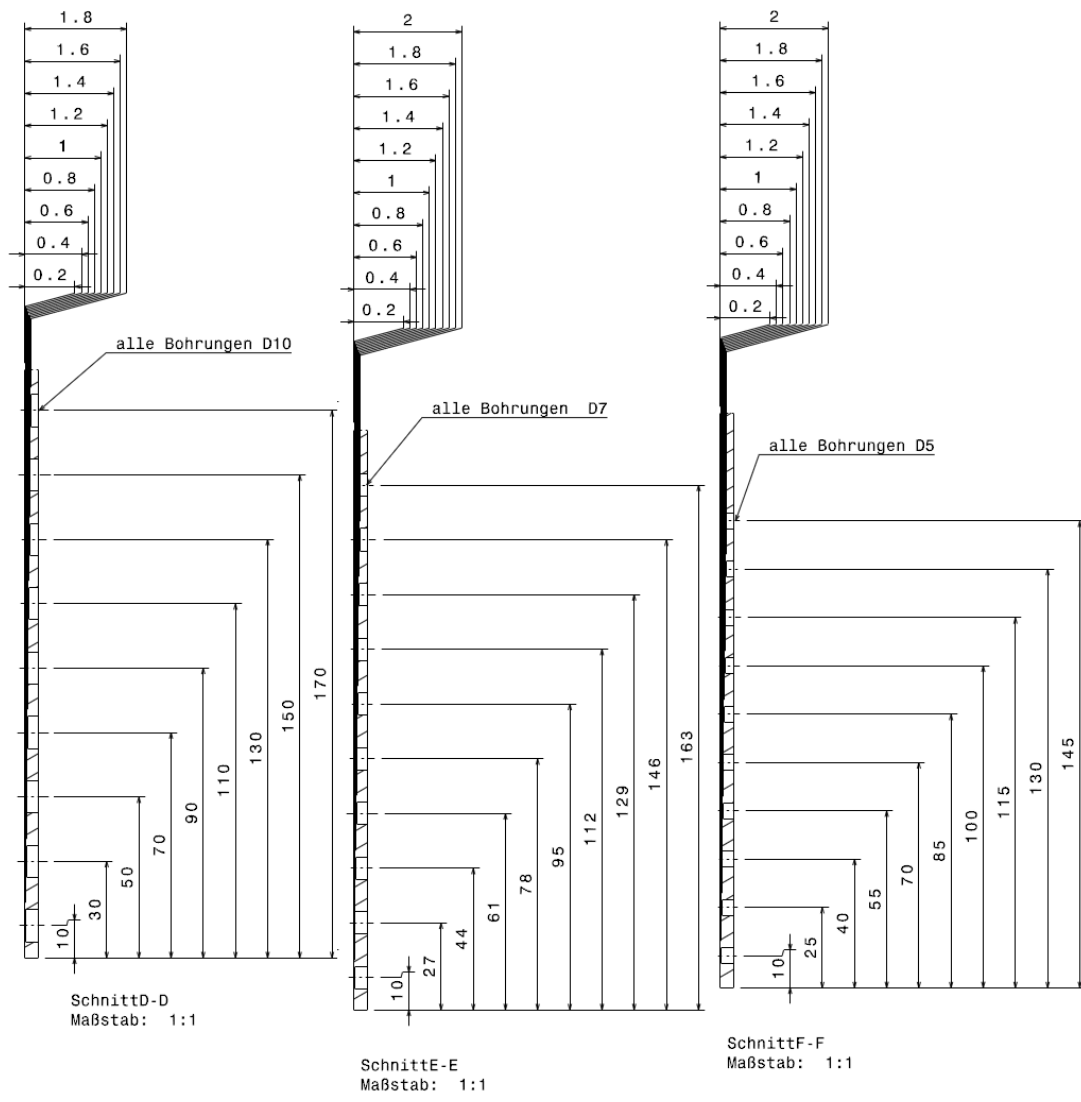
Mechanische Bearbeitung: Schnitte II
